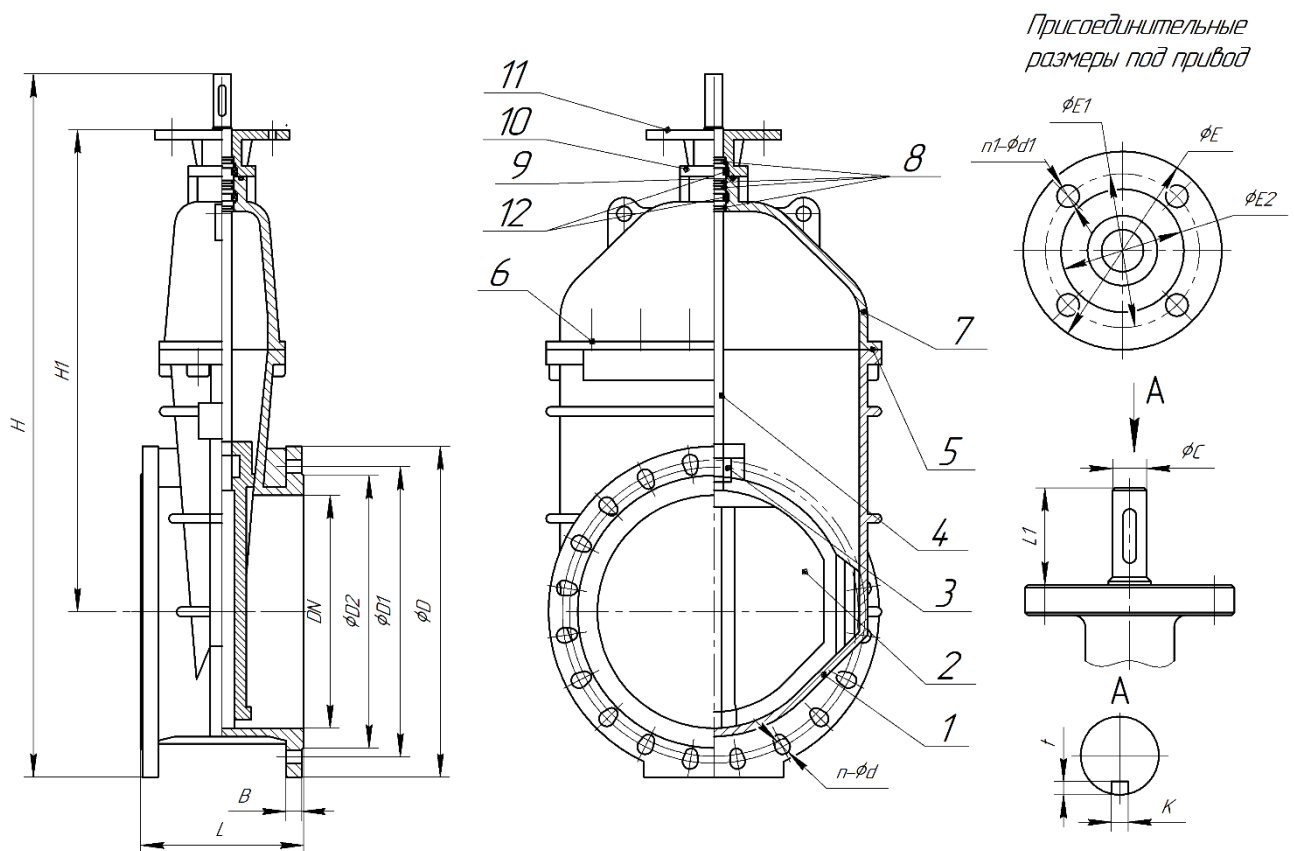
Задвижка 47GVA.Z без исполнительного механизма DN900-1200
